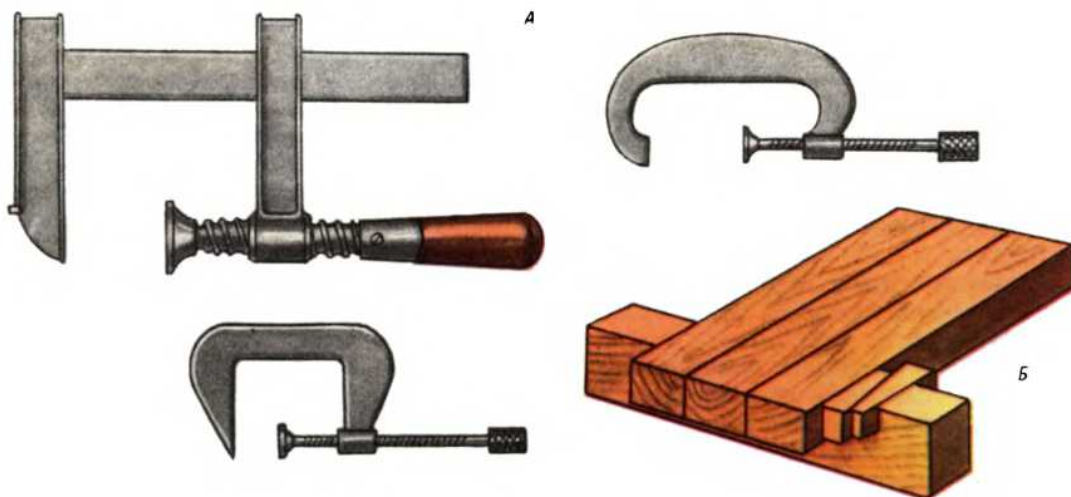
Сжимающие приспособления: А — струбцины; Б — вайма.
